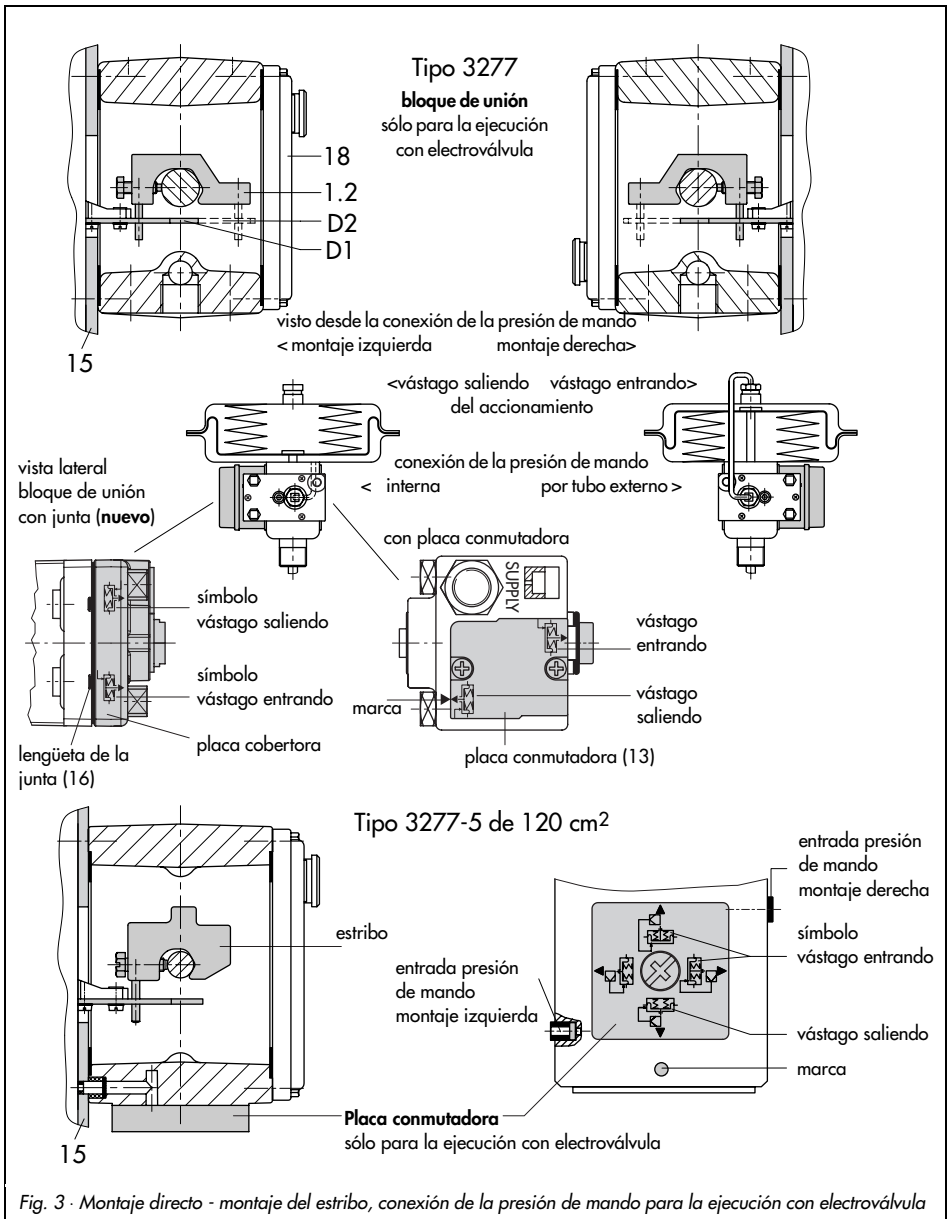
· Montaje directo - montaje del estribo, conexión de la presión de mando para la ejecución con electroválvula
